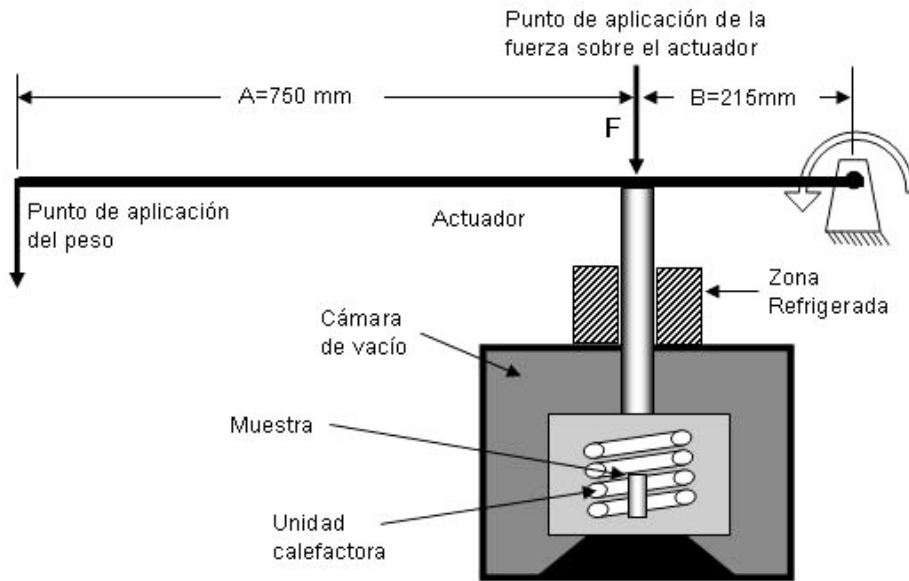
Esquema del equipo de soldadura por difusión en alto vacío.
